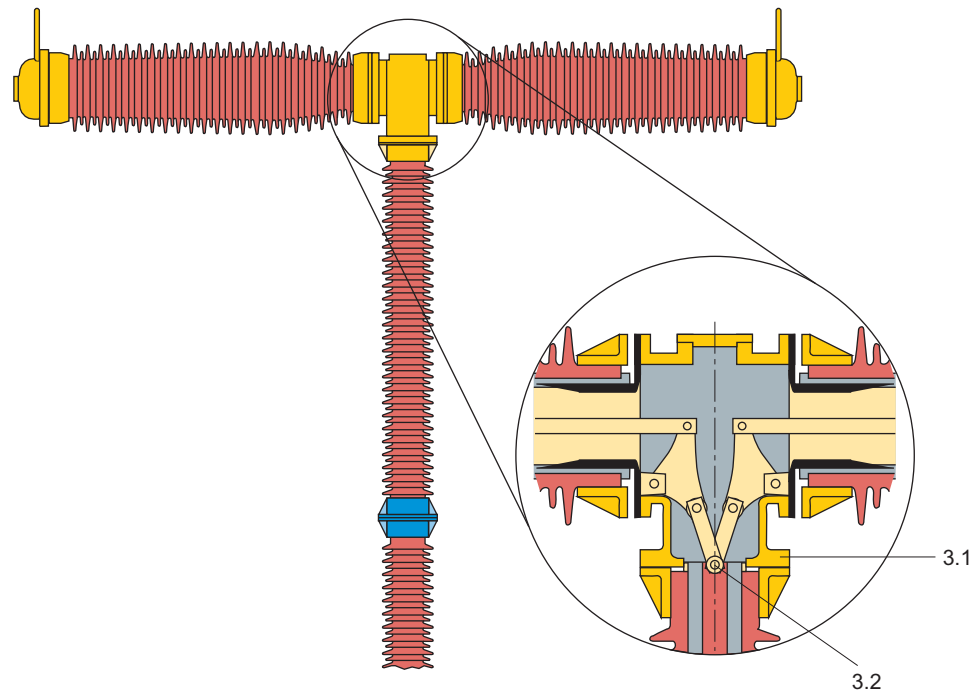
Lageplan für Verbindungs- und Dichtungselemente
